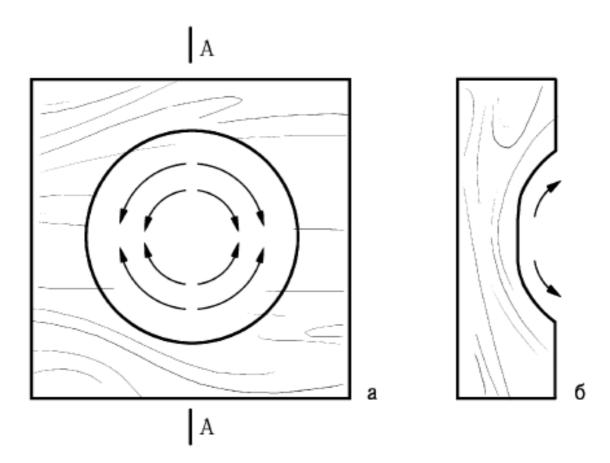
Выполнение круглой вогнутой выемки на торце заготовки первым способом (стрелками показано направление движения инструмента): a – вид сверху;  $\delta$  – вид сбоку Второй способ (рис. 58) осуществляется другим инструментом – клюкарзой, при этом резьбу выполняют от центра к краям. Линии реза могут быть прямыми и несколько изогнутыми (рис. 59).
